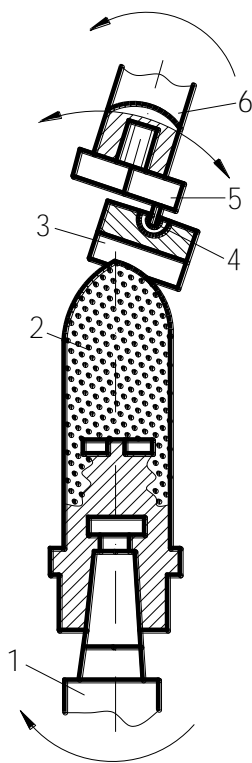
Схема полирования вогнутой поверхности заготовки линзы
